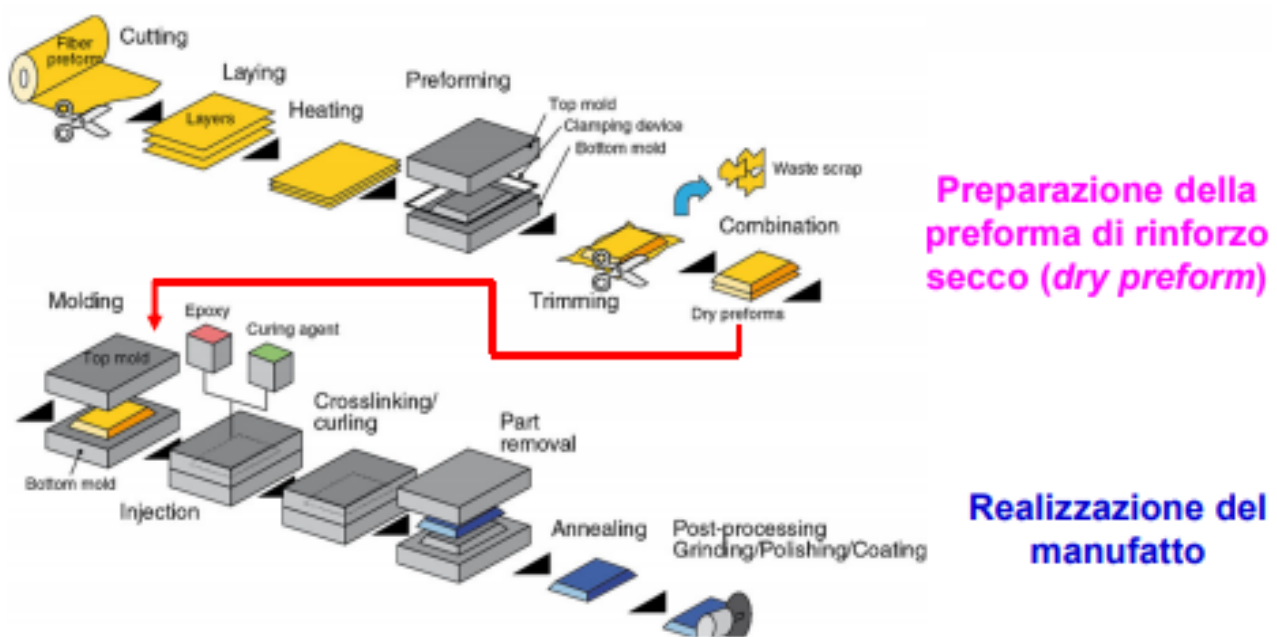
Schema di processo del Resin Transfer Moulding
